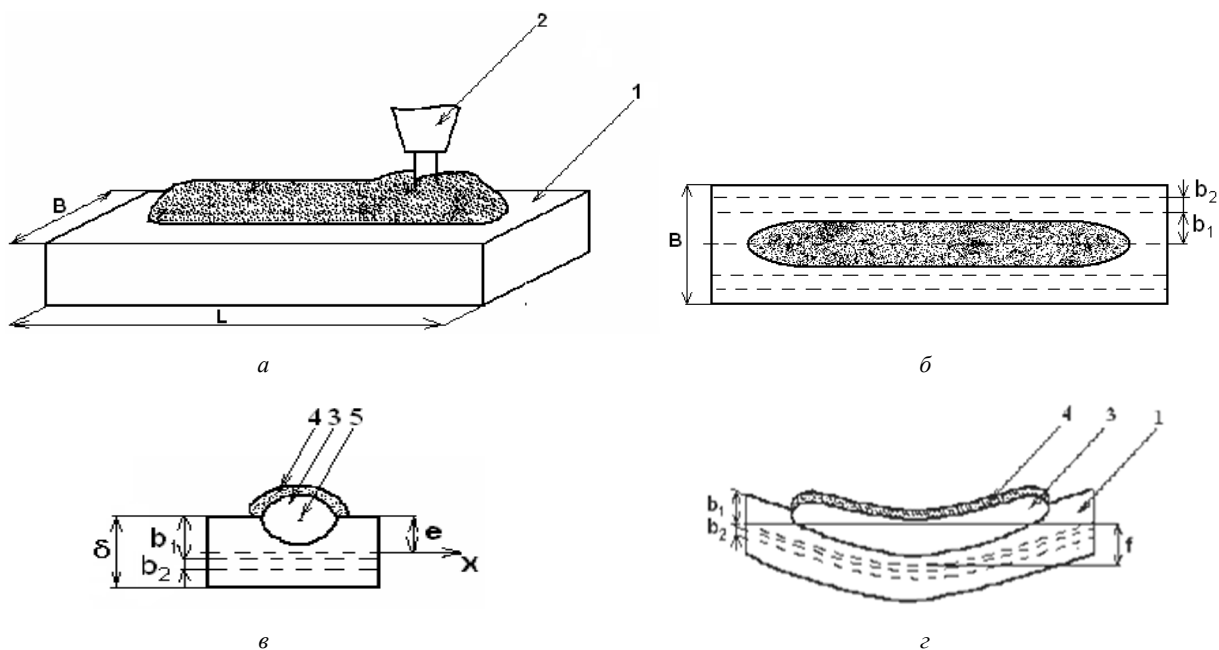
Дослідний зразок у вигляді пластини в процесі зварювання (а), вигляд пластини зверху (б), поперечний переріз пластини із зварним швом та шлаковою коркою (в) та пластини із швом та шлаковою коркою після зварювання та деформації (г), де: 1 – пластини, 2 – зварювальна головка, 3 – зварний шов, 4 – шлакова корка, 5 – точка дії усадочної сили; δ – товщина пластини, e – відстань від точки дії усадочної сили до центра ваги поперечного перерізу пластини, B – ширина пластини, L – довжина пластини, b_1 – ширина зони пластичних деформацій скорочення на стадії нагріву, b_2 – ширина зони пружно-пластичних деформацій скорочення на стадії нагріву, f – величина вигину поздовжньої осі пластини
